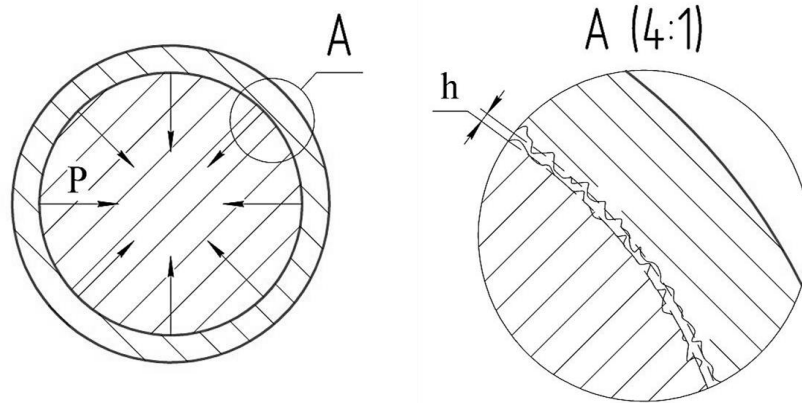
Схема прессового соединения с механическими напряжениями и шероховатостью поверхности на границе сопряжения
